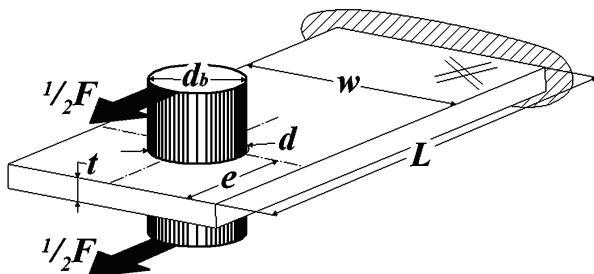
Ламинатный образец с отверстием, нагруженным через стержень
